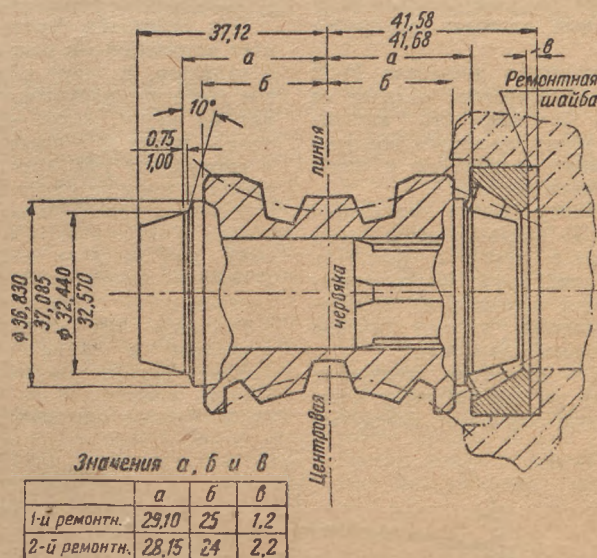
Сопряжение червяка и неподвижного подшипника с постановкой шайбы.
